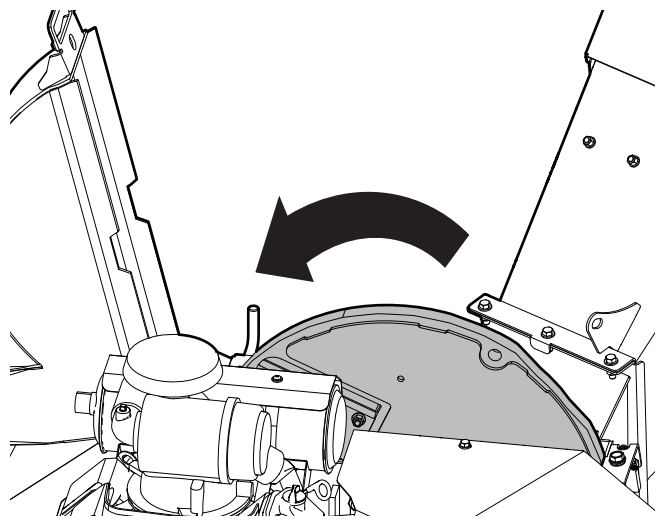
Ouvrez le boîtier supérieur du rotor
